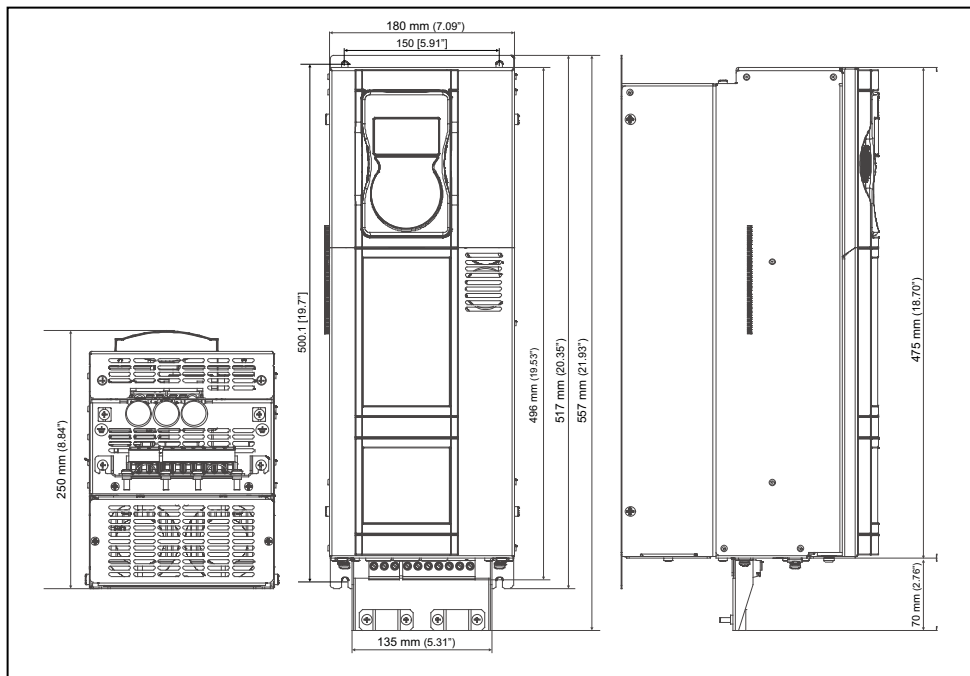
Размеры для типоразмера 3 (ADV200-...-4)
